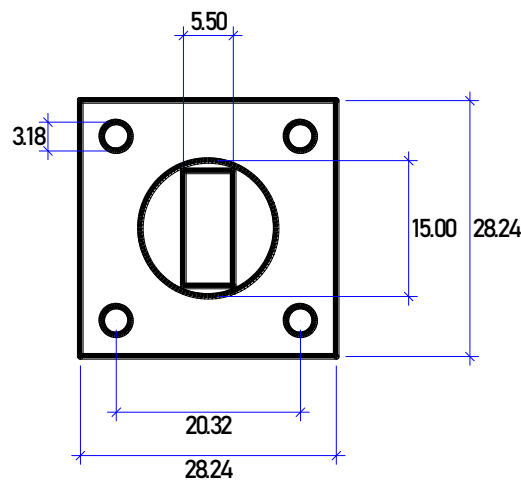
Dimensión de la placa base del dissipador seleccionado 17130
